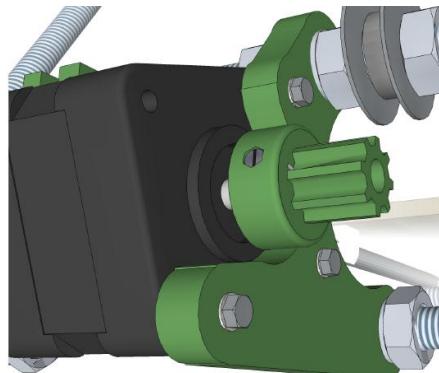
Ajuste de medidas exteriores y ensamblado del eje Y (paso 9). Motor Y ensamblado
